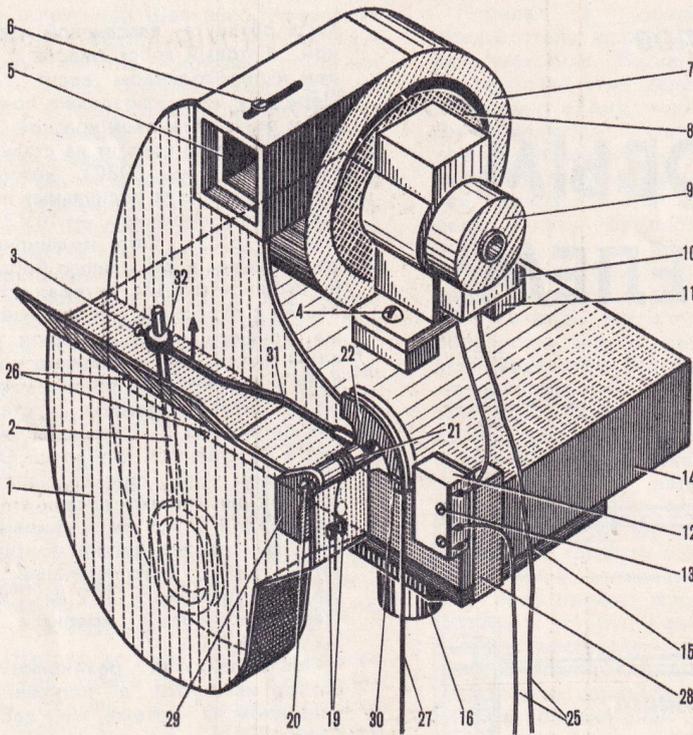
Термометруказатель (без стойки): 1 — бак вертикальный; 2 — рамка; 3 — винт; 4 — винт; 5 — выходной патрубок; 6 — винт М2; 7 — корпус вентилятора; 8 — крыльчатка вентилятора; 9 — двигатель; 10 — планка; 11 — полистироловая колодка; 12 — микропереключатель; 13 — винт; 14 — бак горизонтальный; 15 — полистироловая плата; 16 — фланец; 17 — гайка; 18 — винт; 19 — крепление пружины; 20 — ось (винт М3); 21 — возвратная пружина; 22 — кулачок; 23 — место пайки; 24 — трубка; 25 — электропроводка; 26 — отверстия; 27 — трос; 28 — плата для крепления микропереключателя; 29 — стойки для оси 20; 30 — трубка капиллярная; 31 — рычаг из проволоки; 32 — головка.
